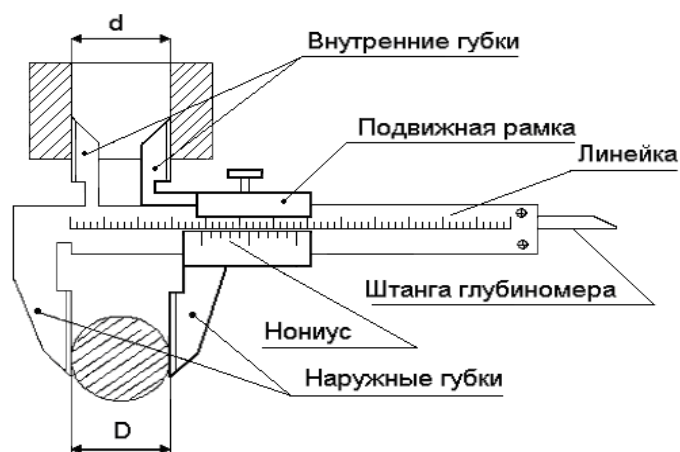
Штангенциркуль типа ШЦ-1.
